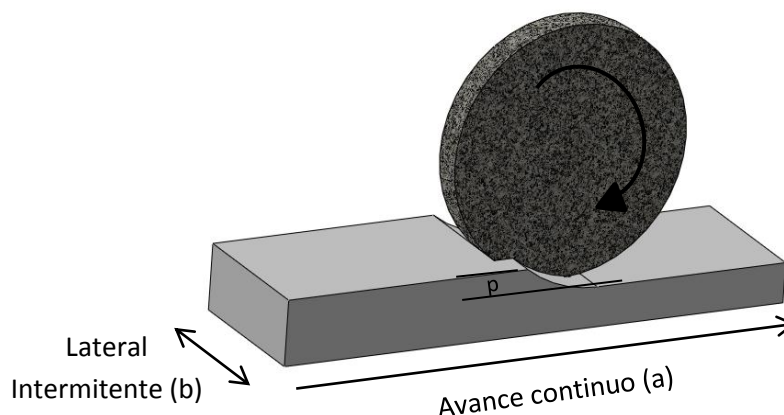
Geometría de corte en rectificado: tangencial plano
